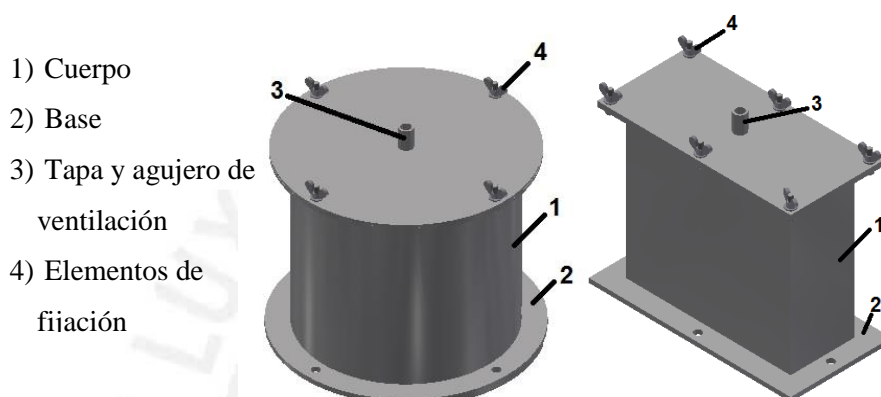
Los moldes y sus partes. Molde cilíndrico (izquierda), Molde prismático rectangular (derecha).
